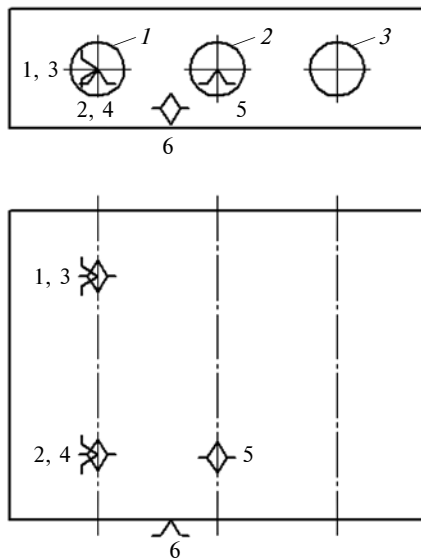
Схема базирования корпусной детали на первой операции: 1, 2, 3, 4 — двойная направляющая база; 5, 6 — опорные базы
